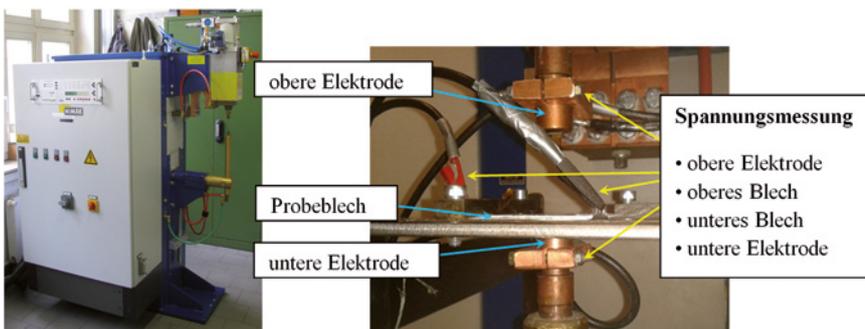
Punktschweißmaschine (links) und Spannungsmessung (rechts)
